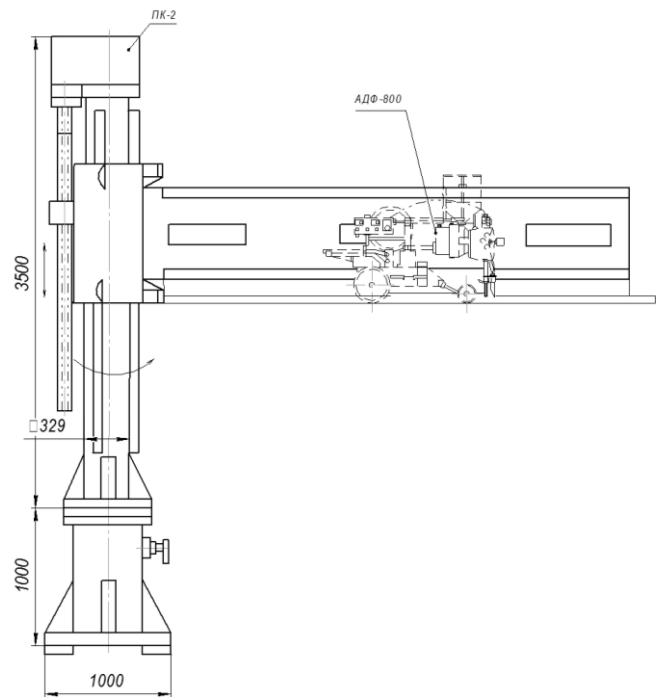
Загальний вигляд колони для закріплення зварювального автомата
